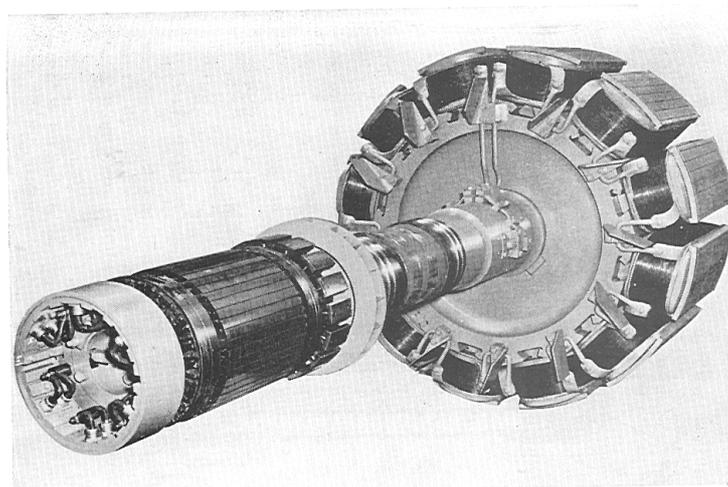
b - Rotore di macchina sincrona con eccitatrice coassiale.
